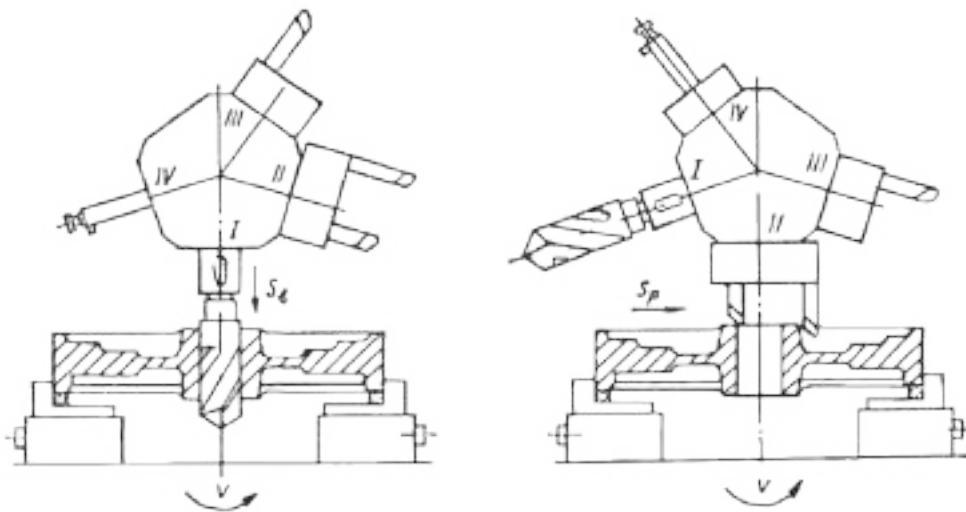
Зразок обробки деталі «Шків» на токарно-карусельному верстаті
